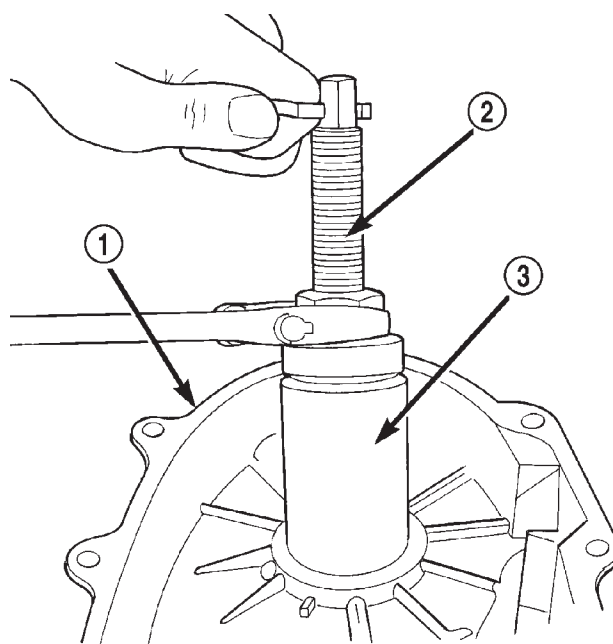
Desmontaje del cojinete trasero del eje transmisor
